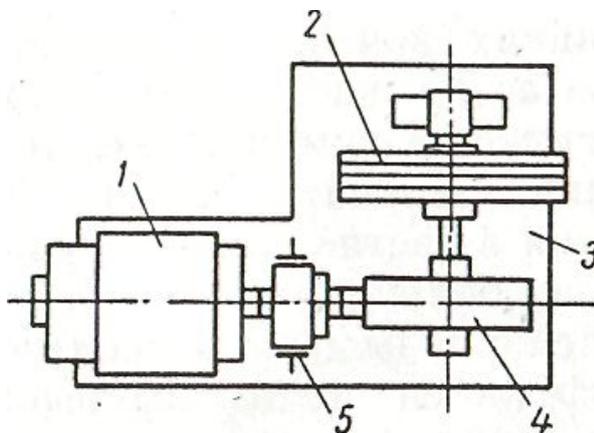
Схема редукторной лебедки с канатоведущим шкивом
